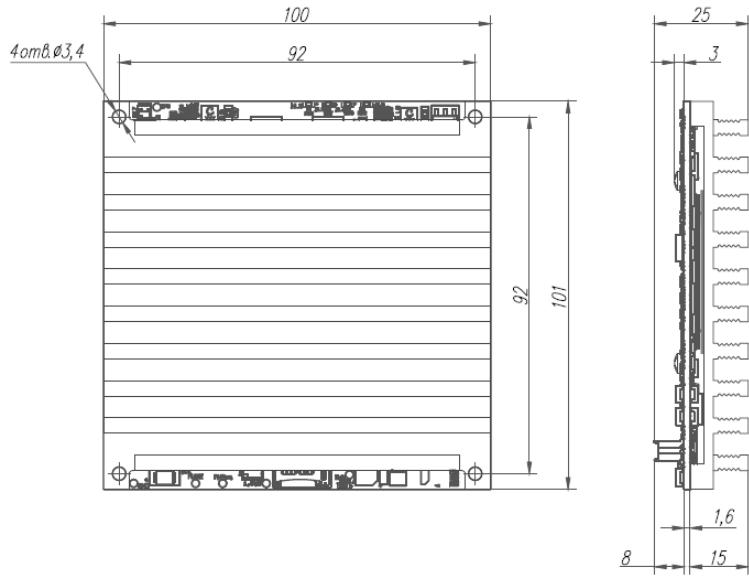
Габаритные и присоединительные размеры Модуля
